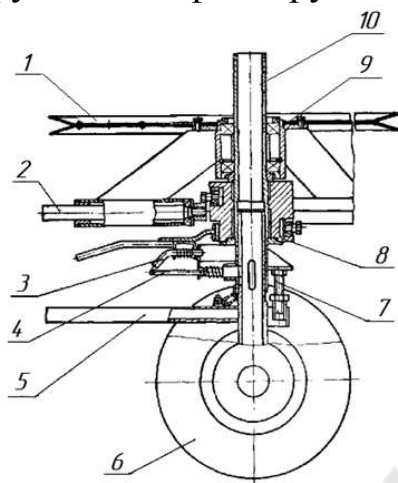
Ротор левый: 1 – шкив; 2 – ось граблин; 3 – фиксатор; 4 – стопор; 5 – ручка; 6 – ход колесный; 7 – болт регулировочный; 8 – копир; 9 – корпус; 10 – ось
